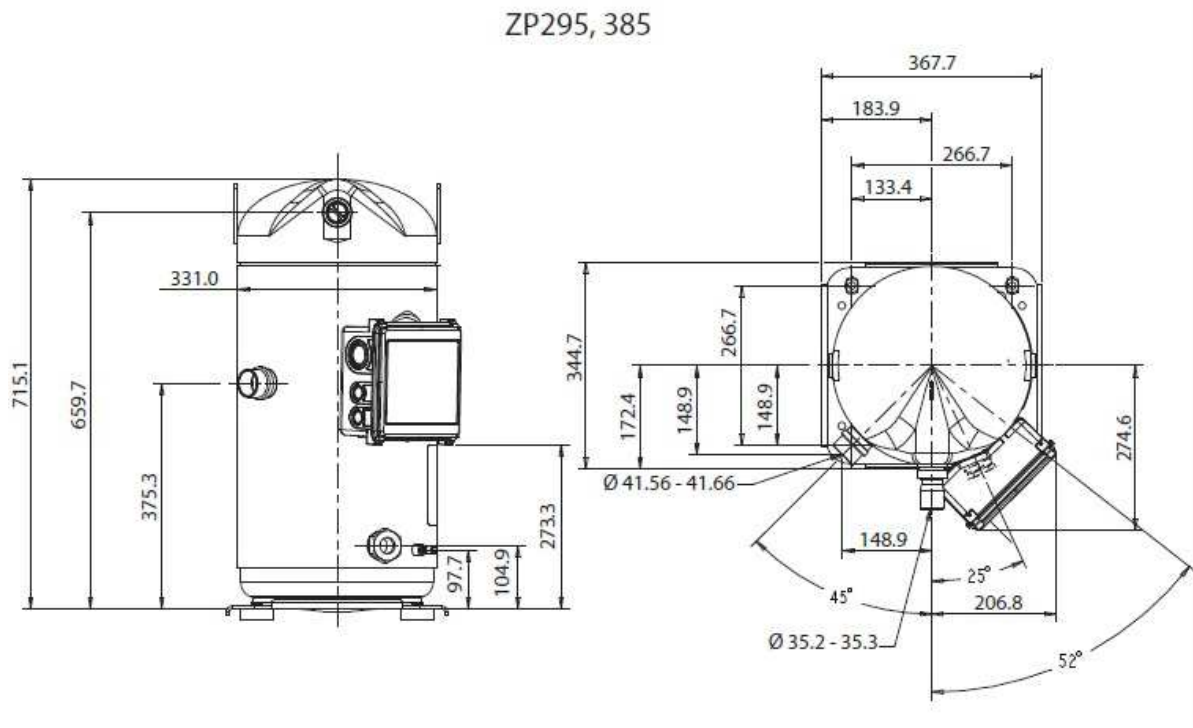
Disegno CAD del compressore ZP295KCE-TWD
